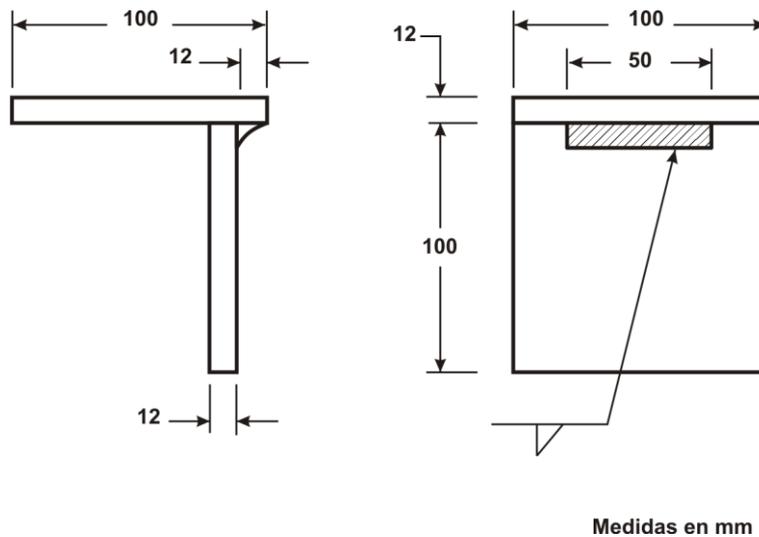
Probeta de rotura para soldadura de filete – Calificación de soldador punteador.
